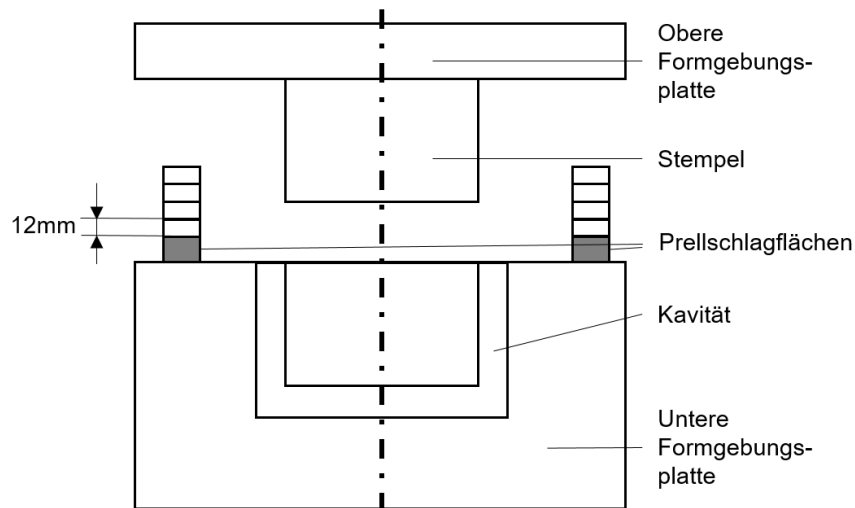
Prinzipskizze des Werkzeugaufbaus für die Step-Shot-Versuche
